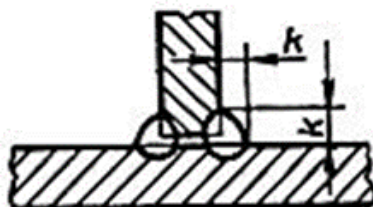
Сварной шов соединения ТЗ
